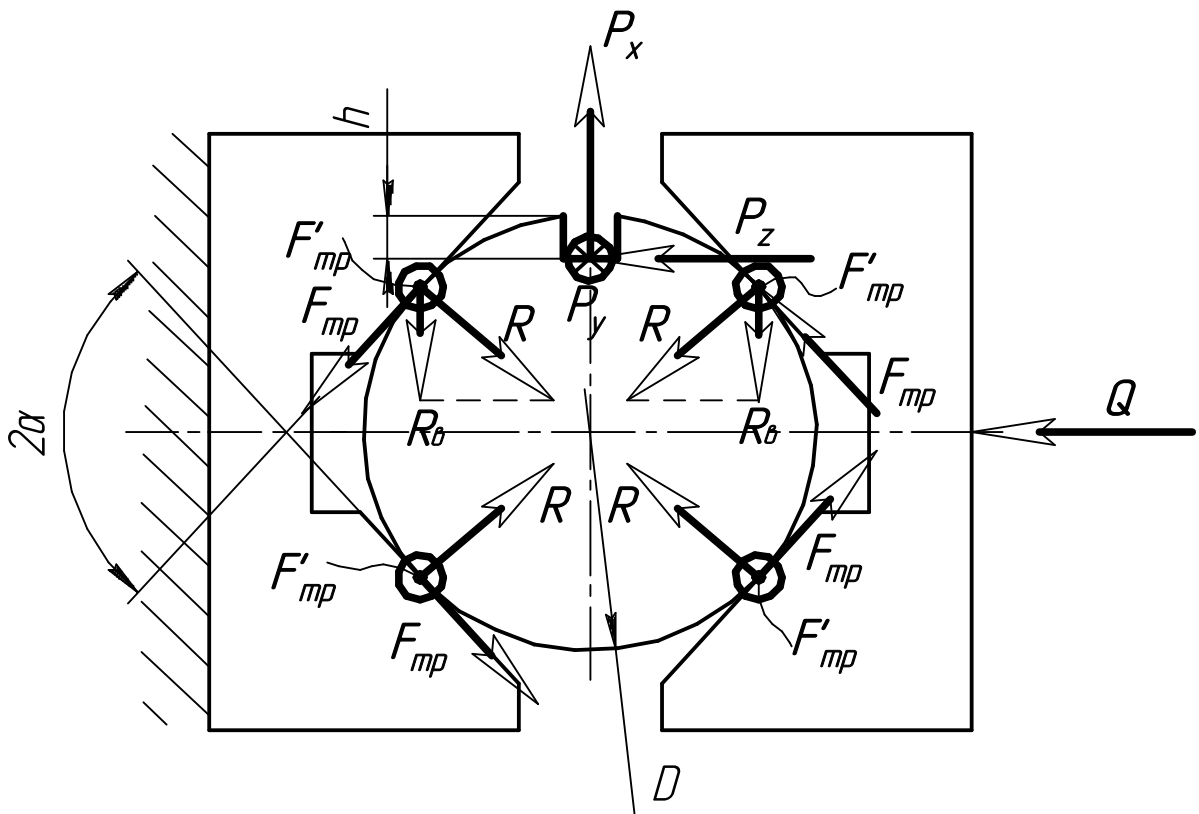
Розрахункова схема для визначення зусилля закріплення деталі при фрезеруванні шпонкового пазу кінцевою фрезою
